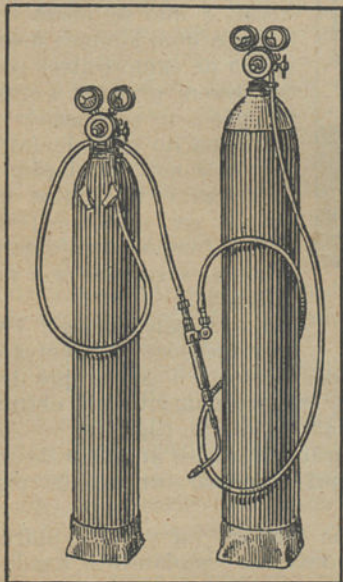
Poste de soldadura autogênea utilizando o acetileno dissolvido.
